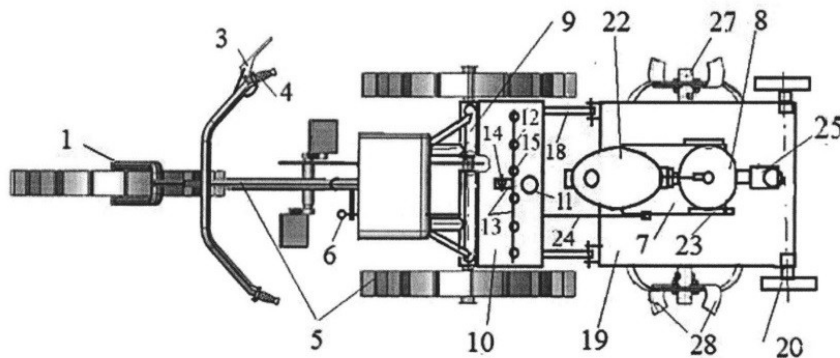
Схема агрегата для подготовки почвы под посадку риса в Бурунди — общий вид сверху агрегата
